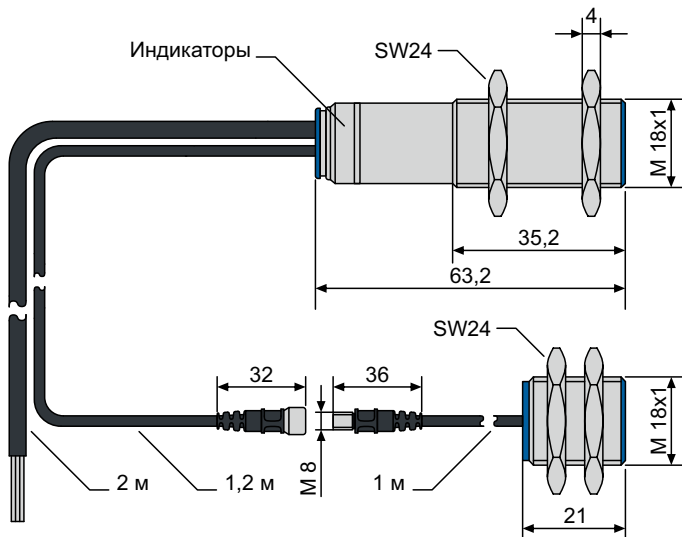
Габаритные размеры датчиков dbk+4/...
